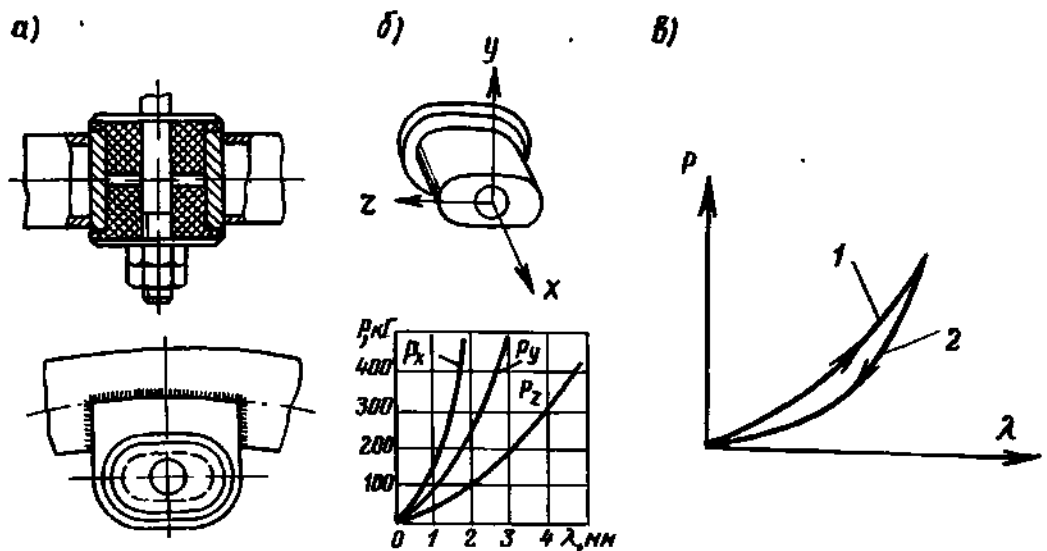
Резиновый демпфер крепления поршневого двигателя: а — конструкция; б — механические характеристики; в — гистерезис при циклическом нагружении; 1 — нагружение; 2 — разгрузка
